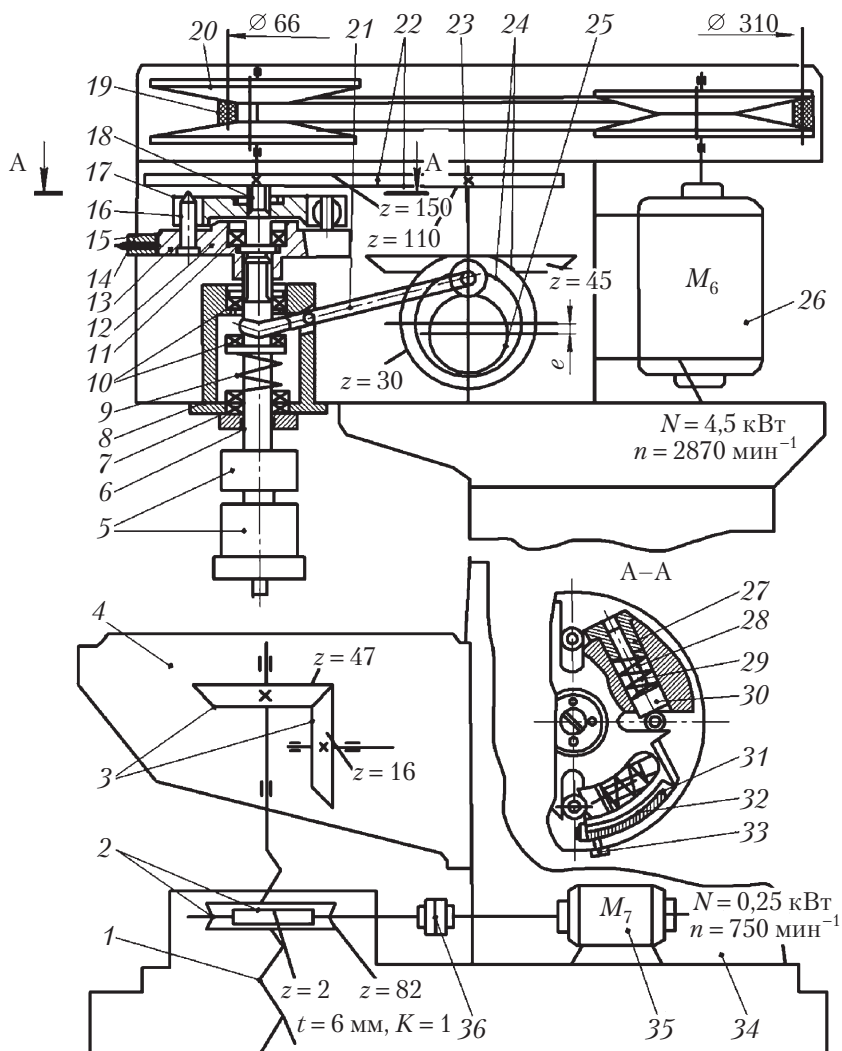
Схема виброустановки ВУ-6 на базе вертикально-сверлильного станка мод. 2А135
